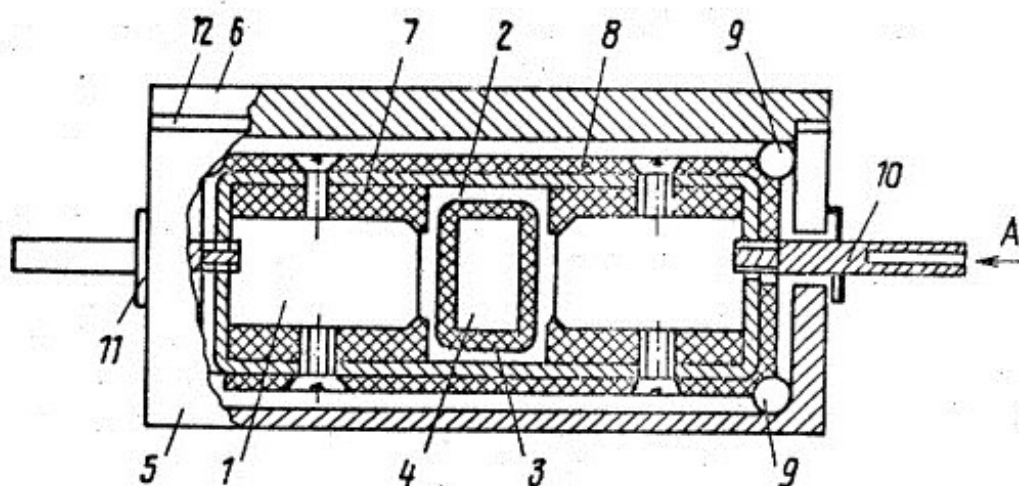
Конструкция линейного магнитоэлектрического двигателя
